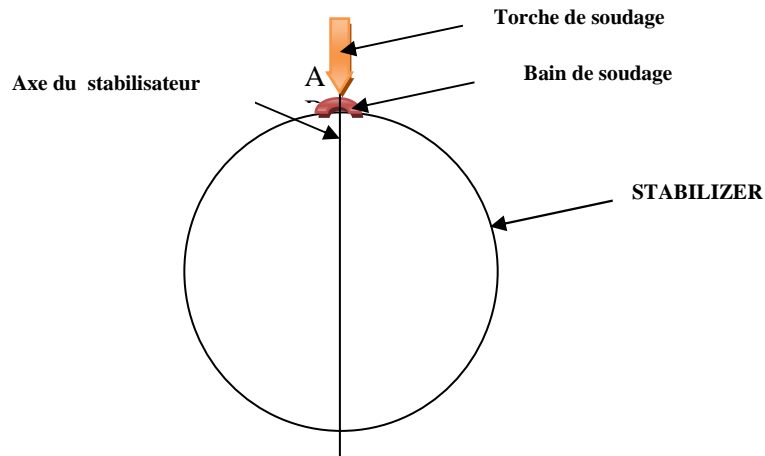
Risque de coulée de bain de soudage limité [41]
